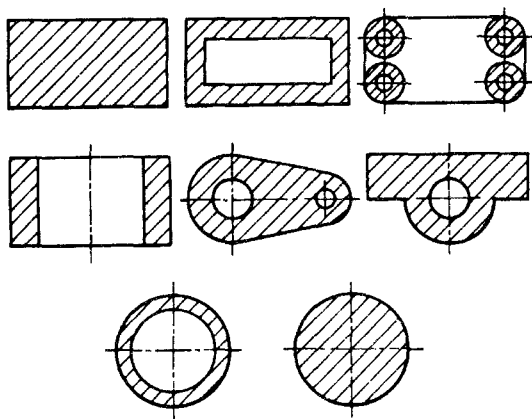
Примеры поверхностей деталей, обрабатываемых на фрезерных и шлифовальных станках
